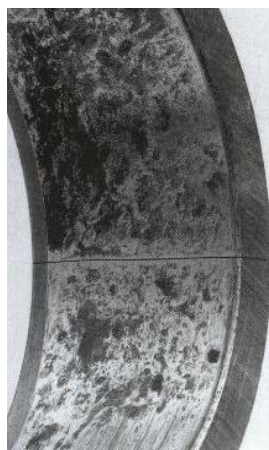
Aro interior de rodamiento de rodillos a rótula con corrosión de contacto y rotura transversal.
